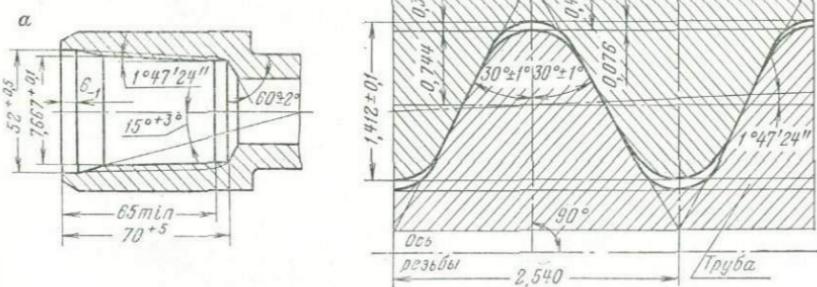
Профили и размеры резьб ниппеля и муфты:
